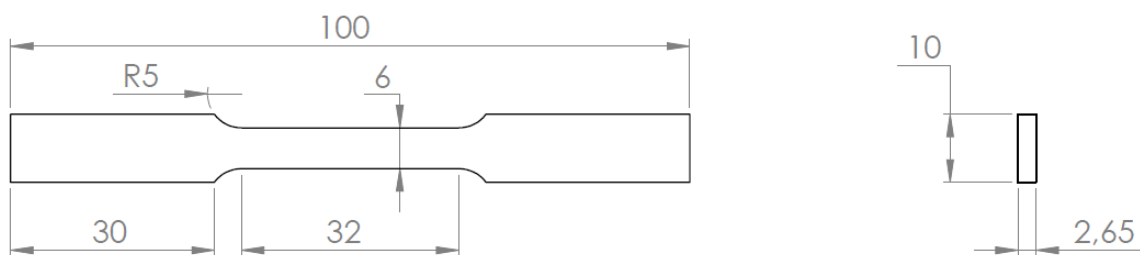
Corpo de prova de tração com dimensões reduzidas. Dimensões em milímetros
